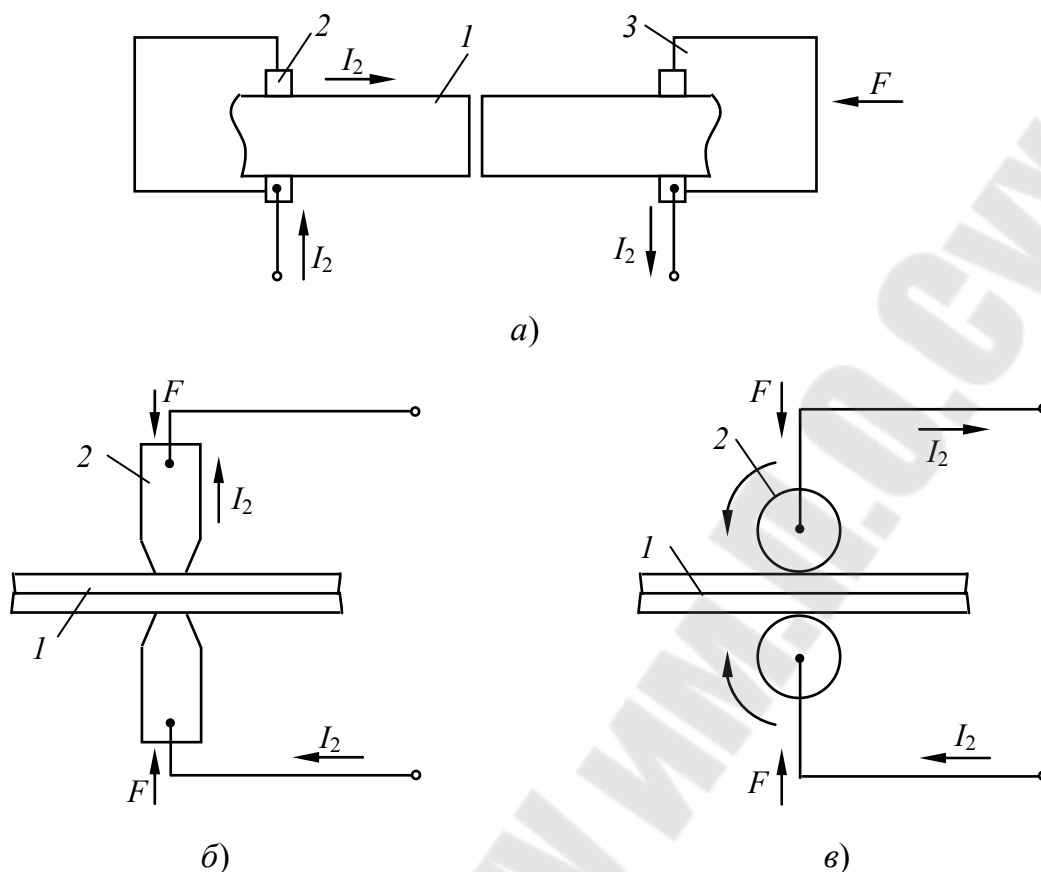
Разновидности контактной сварки: а – стыковая; б – точечная; в – роликовая; 1 – деталь; 2 – зажимной токоподводящий контакт; 3 – контактная перемычка
